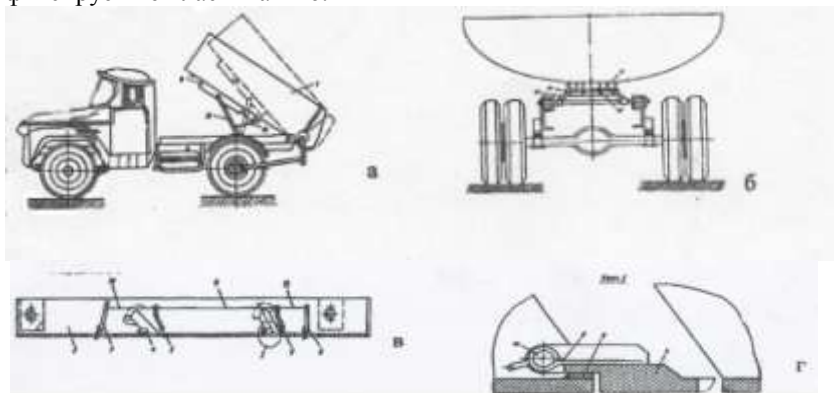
а) Общий вид упорного устройства; б) Вид сбоку упорного устройства; в) Направляющая в сборке; г) Узел 1 на рис (в).
